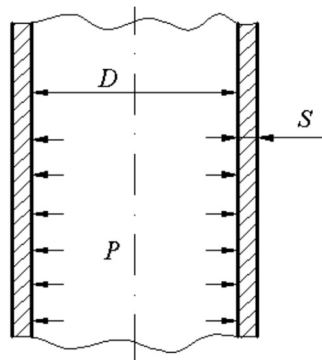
Схема циліндричної обичайки корпусу апарата
